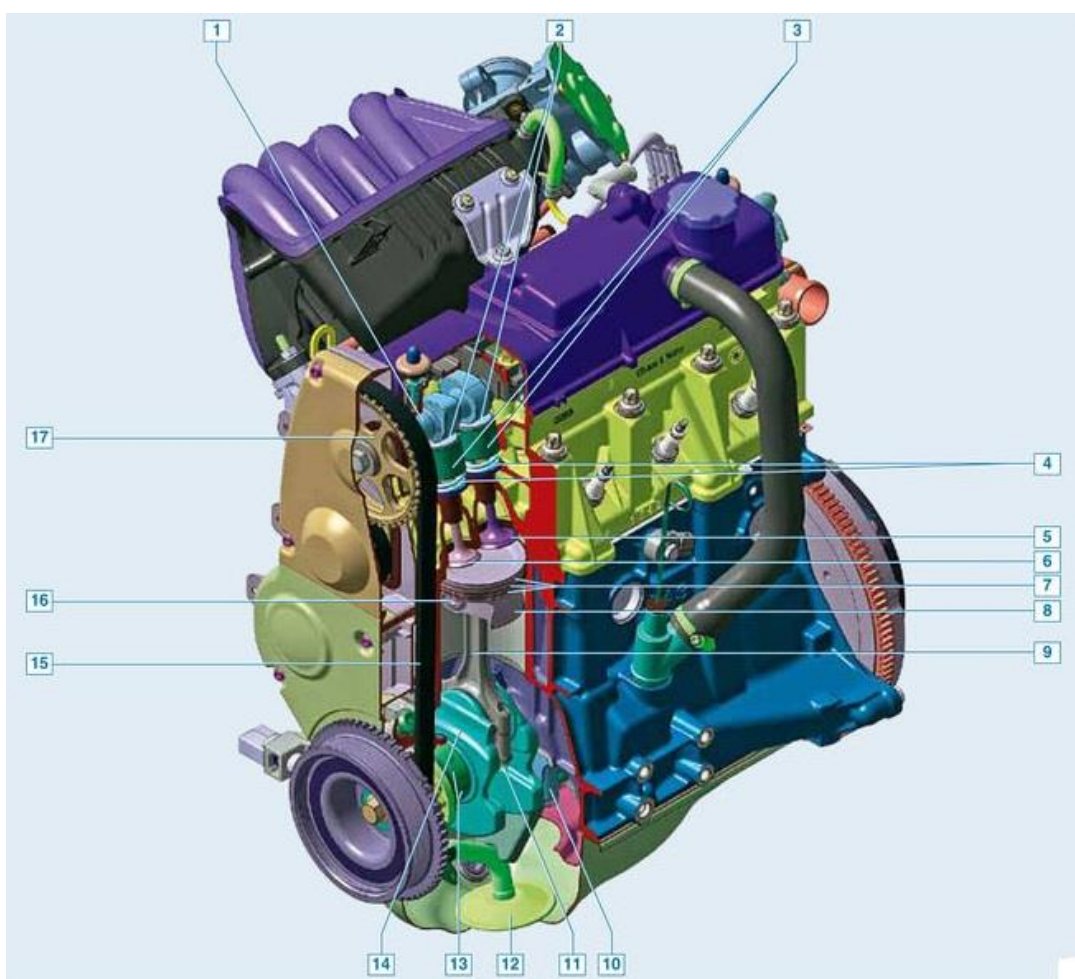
Общий вид двигателя автомобиля «Гранта»
